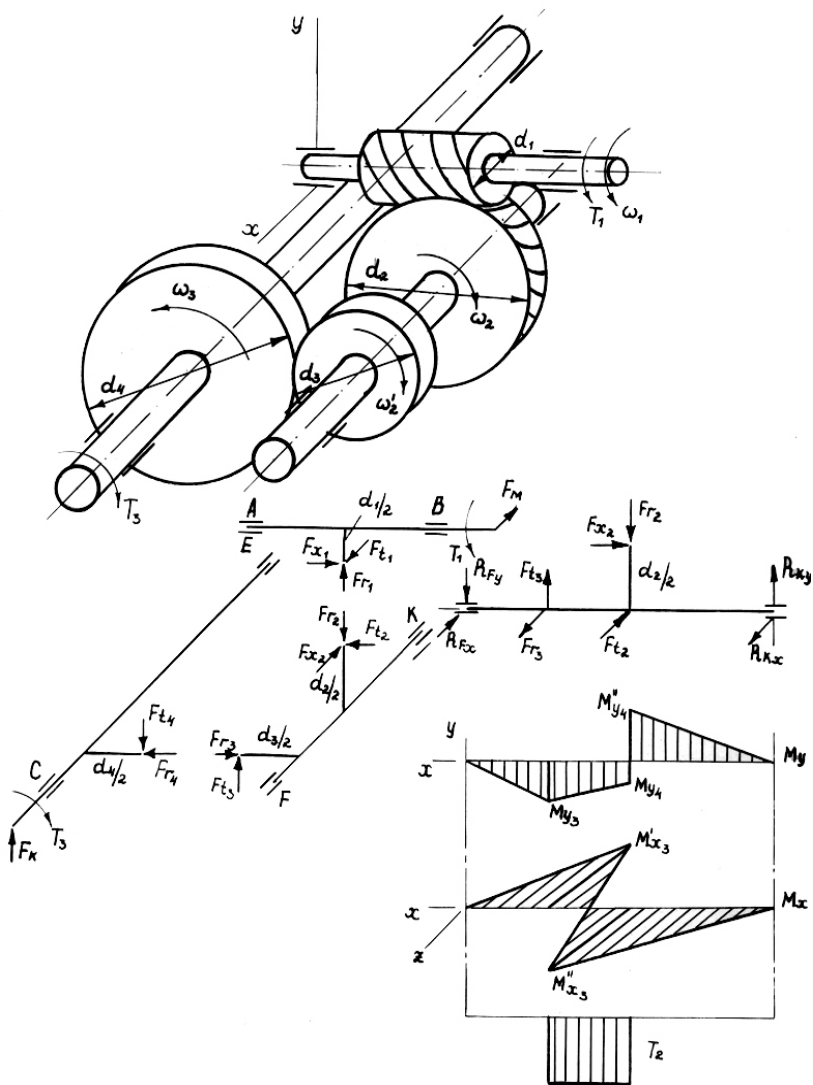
Червячно-зубчатая передача со второй цилиндрической прямозубой ступенью
